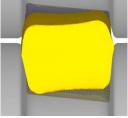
Последний момент процесса прокатки заготовки с величиной ромбичности 20 мм и начальным углом поворота заготовки 6°
